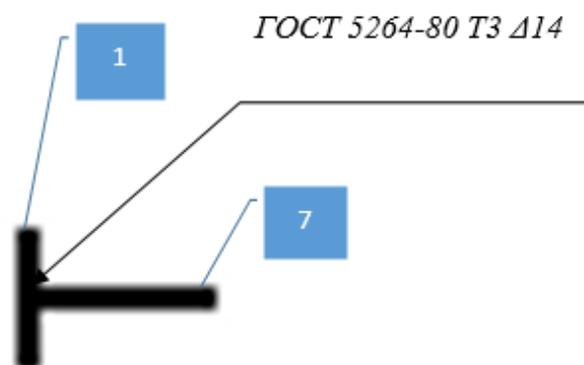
Схема сварки пластин позиция 1 и позиция 7
